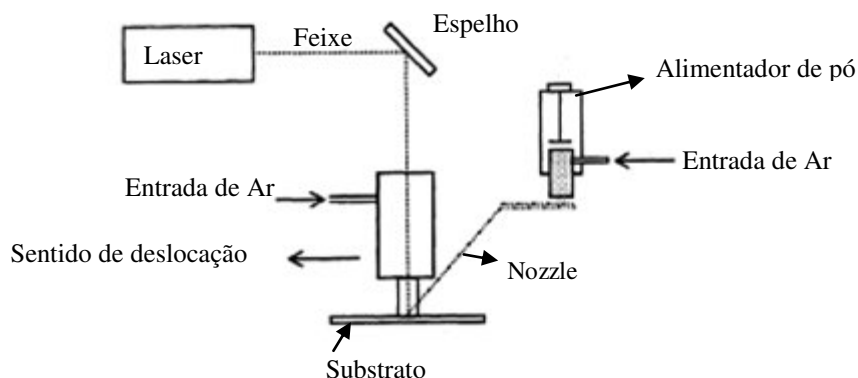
Esquema representativo dos principais componentes de um sistema laser cladding {adaptado de [8]}.
